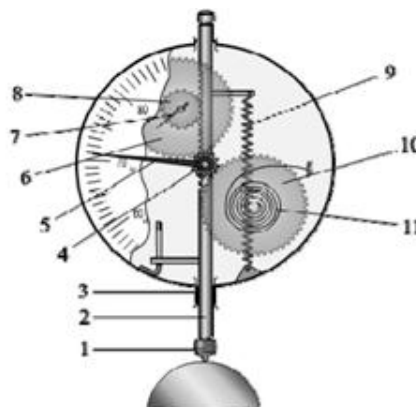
Пристрій індикатора годинникового типу: 1 – наконечник; 2 – вимірювальний стрижень – рейка; 3 – гільза; 4 – трибка; 5 – стрілка; 6 – передавальне зубчасте колесо; 7 – стрілка; 8 – зубчасте рейкове колесо; 9 – пружина; 10 – зубчасте колесо; 11 – пружинний волосок.
